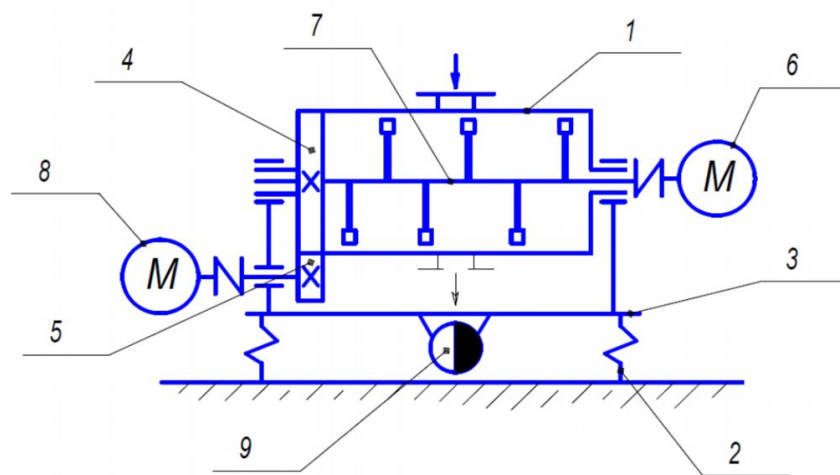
Схема вібраційного змішувача: 1 – робоча камера; 2 – пружина;
